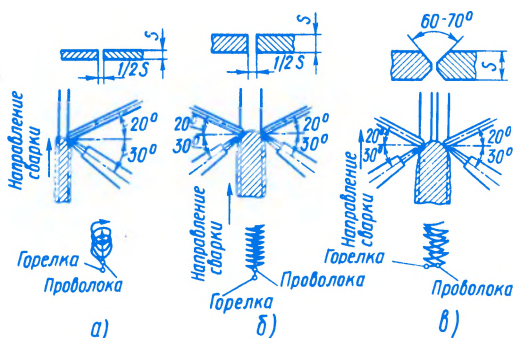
Сварка сквозным валиком при толщине:
